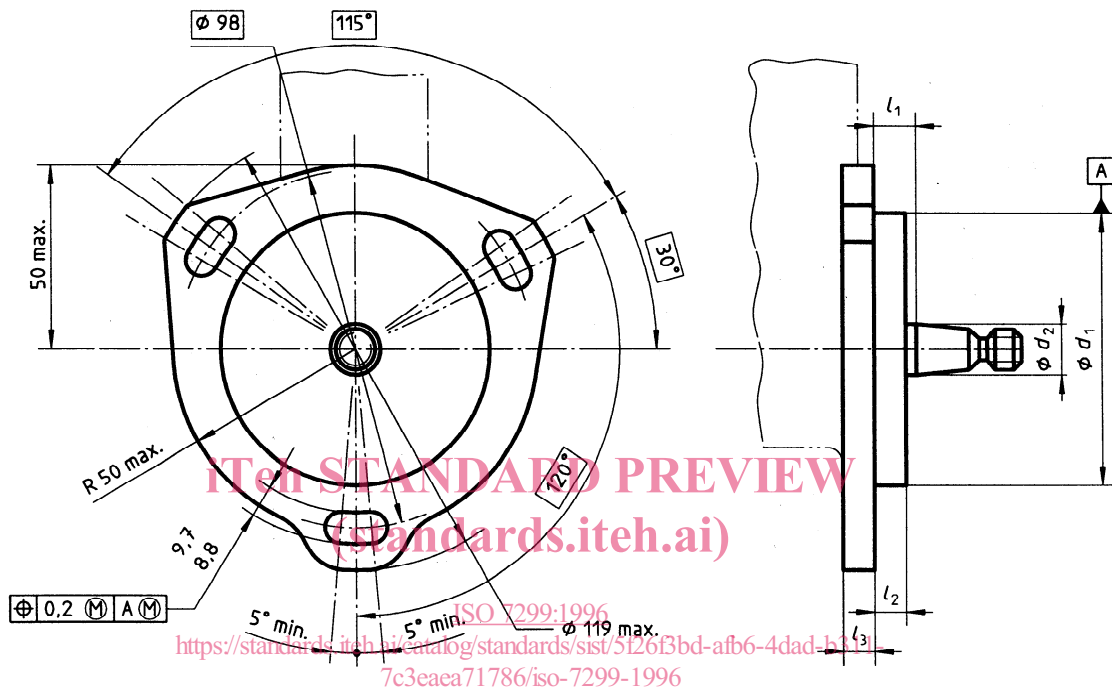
Pompes d'injection de carburant en ligne — Bride de montage de type 5
